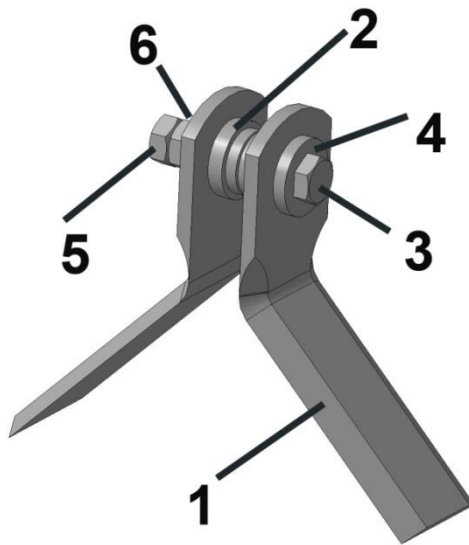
ИРО 03.400Б Нож в сборе (короткий)
